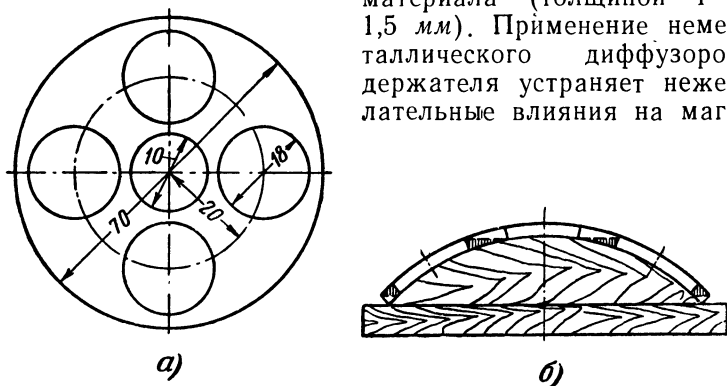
Изготовление диффузородержателя из органического стекла. *а*—заготовка с отверстиями; *б*—формовка диффузородержателя на деревянном шаблоне.
